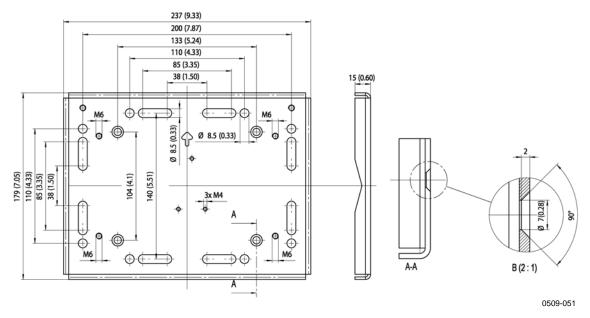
Dimensions de la plage de montage métallique (mm/pouce)
